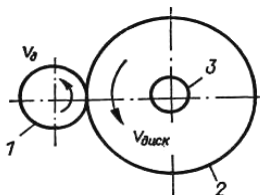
Принципова схема оброблення фрикційним зміцненням циліндричних поверхонь : 1 – деталь, що обробляється; 2 - металевий диск; 3 - шпиндель.
